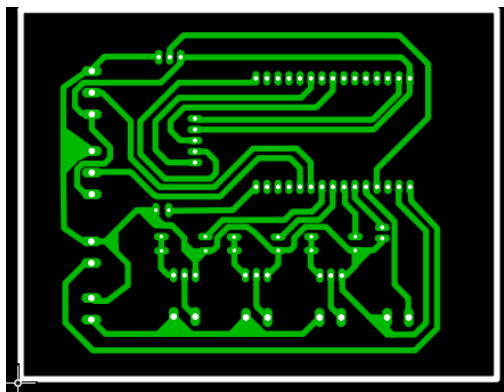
, Diseño PCB Sprint Layout para la Nivelación de pH.
